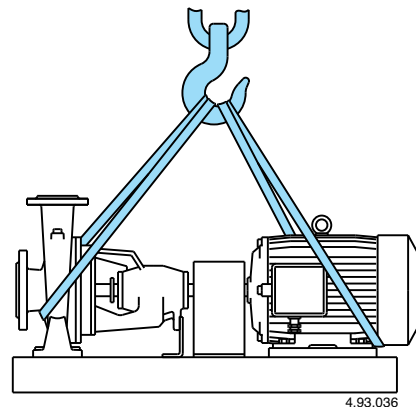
Строповка канатами для поднятия двигатель-насосного агрегата.
